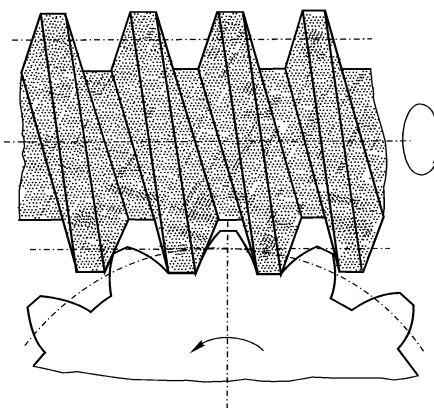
Шлифование зубчатого колеса и использованием абразивного червяка
